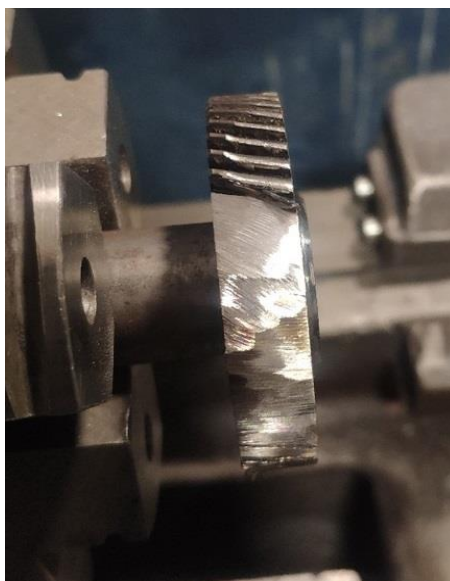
Шестерня с удаленными изношенными зубьями
